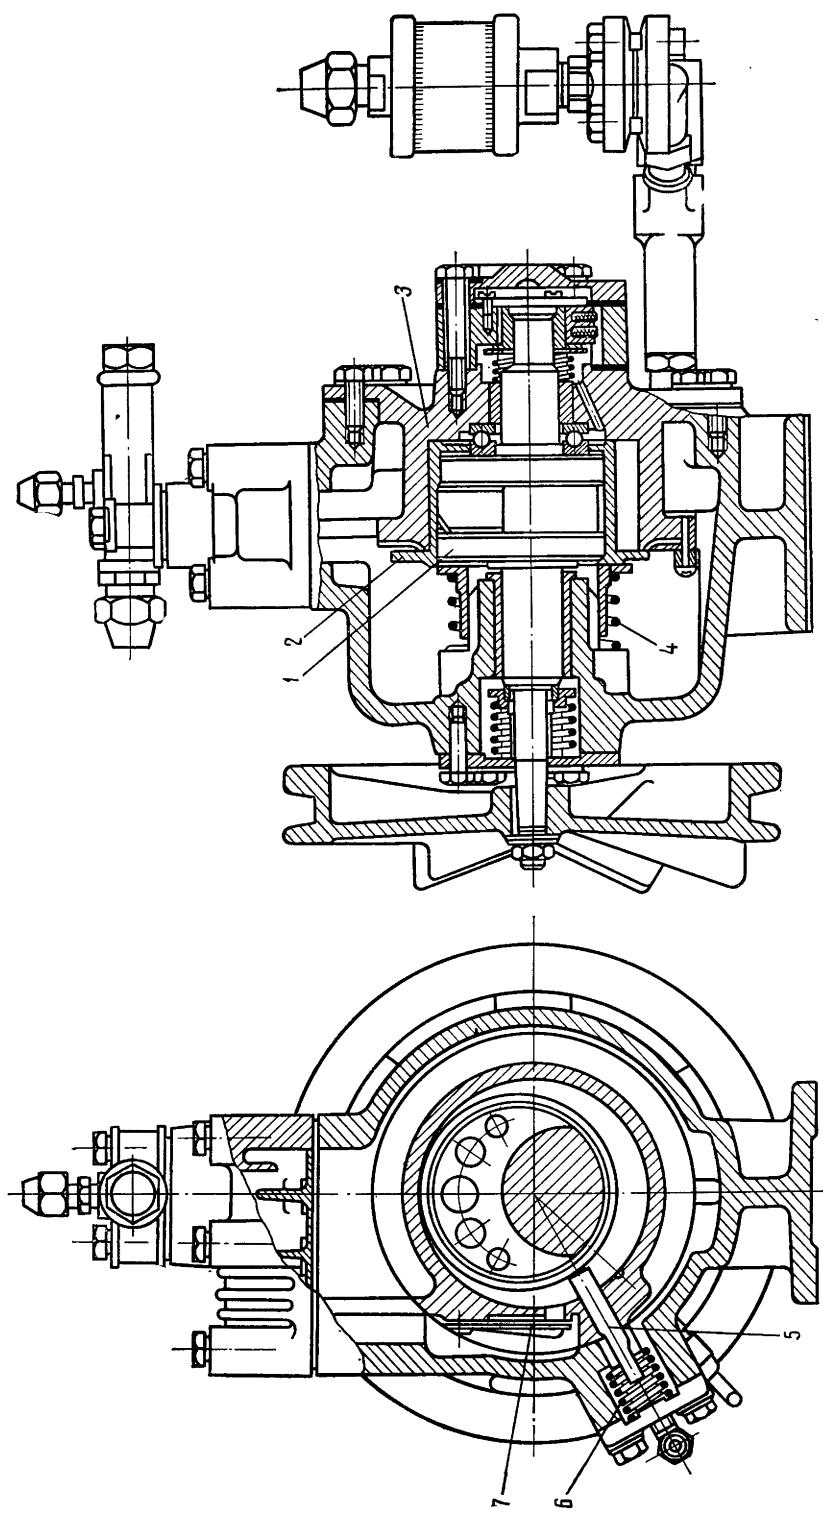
Открытый фреоновый ротационный компрессор ФРУ-600.
